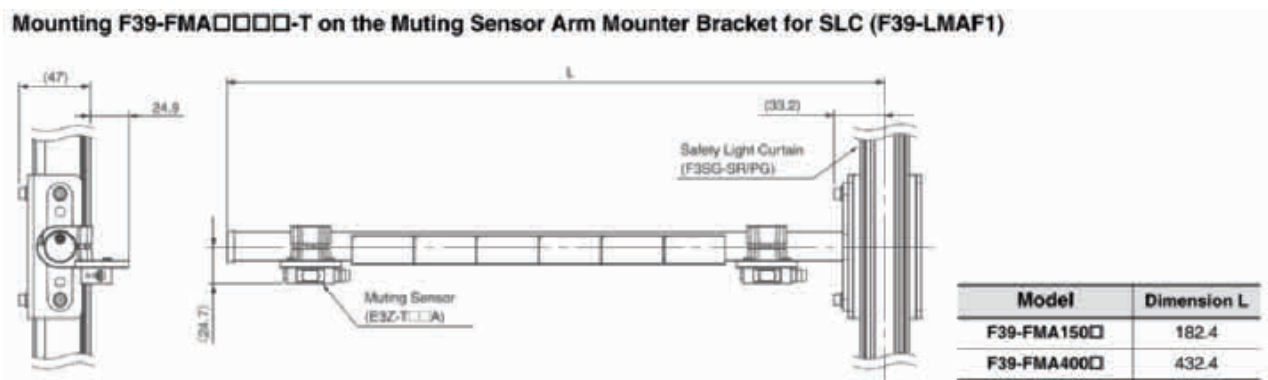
Fissaggio braccetti di muting sulla barriera con staffa F39-LMAF1
